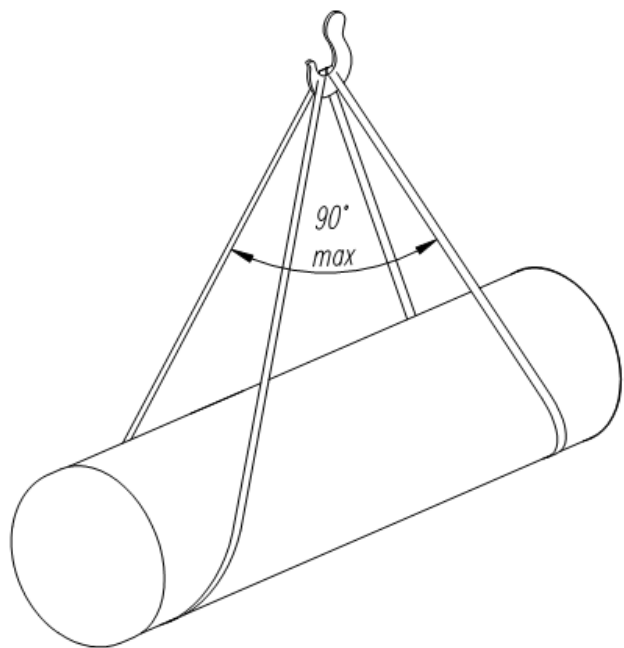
Схема строповки корпуса УО длиной до 4 метров.
